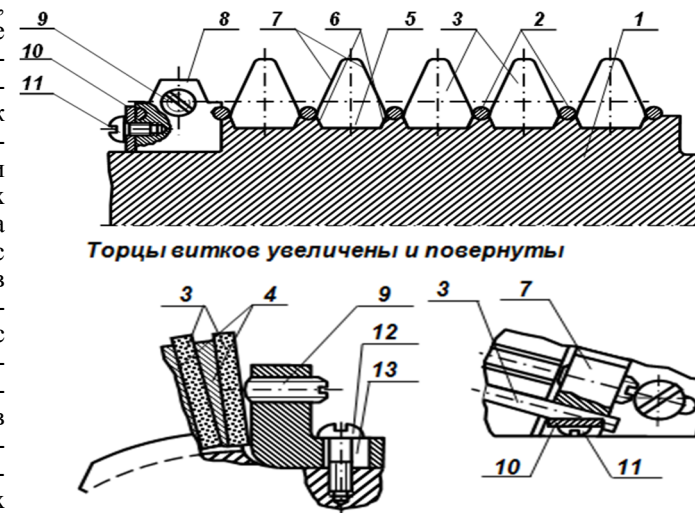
Конструкция сборного червячного зуборезного инструмента с креплением витков, набранных из сменных режущих пластин и клиновидных вставок – пружинами, расположенными у ножек между этими витками
